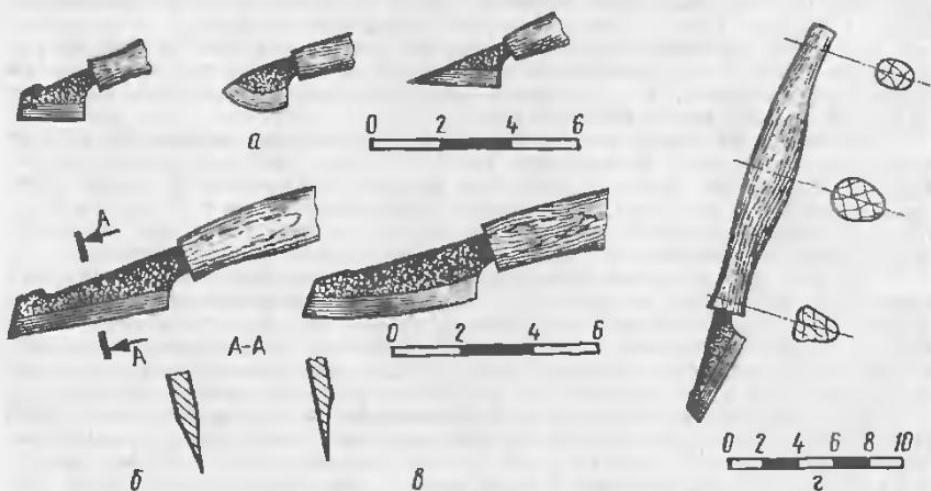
Образцы ножей для модельных работ: а - образцы ножей; б - бритвенная заточка; в - односторонняя заточка; г - форма рукоятки
